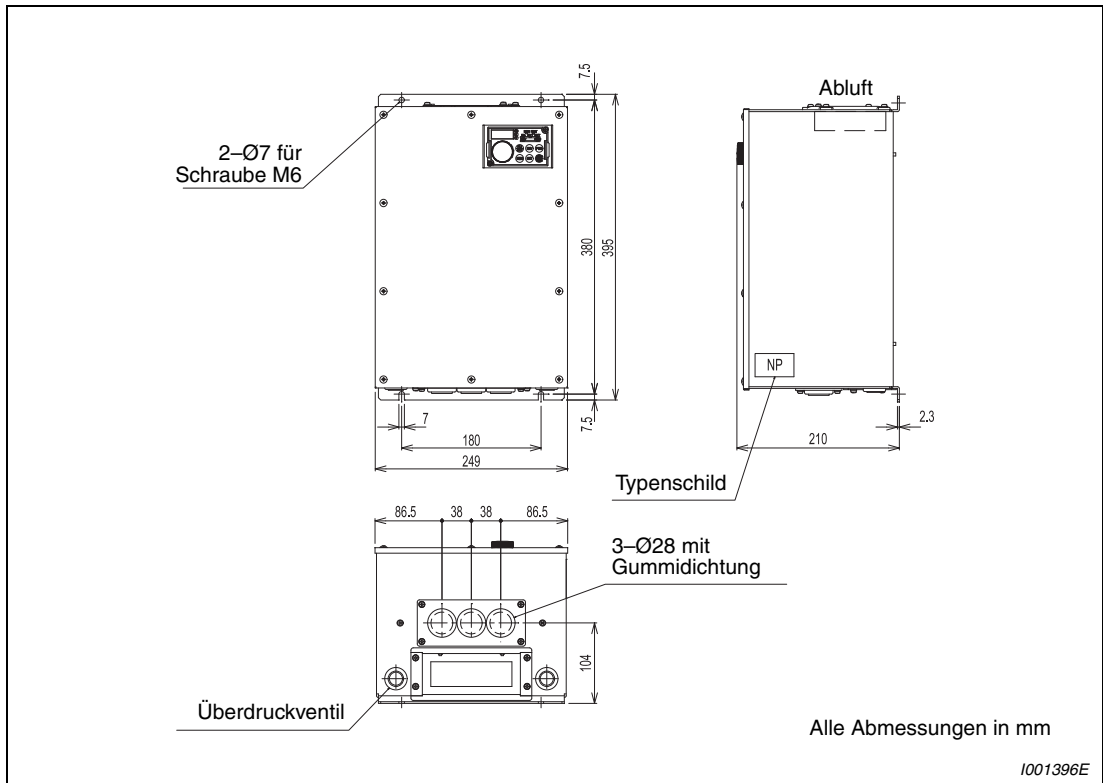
Abmessungen FR-F746-00023 bis -00126
